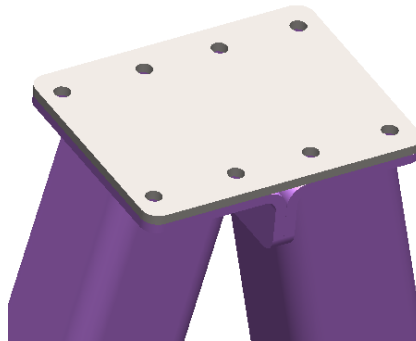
Vista de soldado de pieza N°3 con pieza N°1 (Fuente 89)
